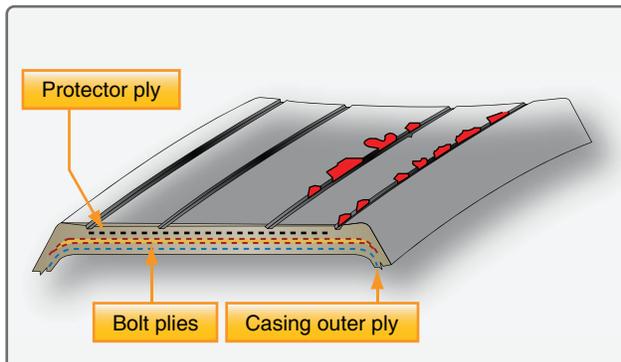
Superfície de rodagem lascada e a segmentação do pneu exige que o pneu seja retirado de serviço, ou se mais de um centímetro quadrado do reforço das camadas ou protetor das camadas estiver exposto.
